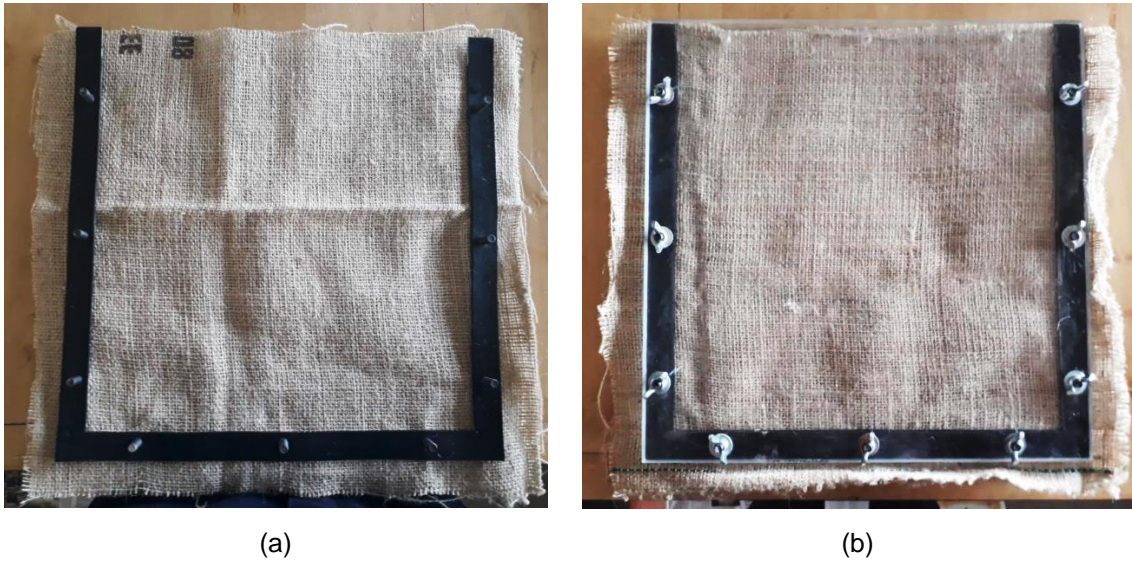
Moldes acrílicos utilizados para a moldagem das placas: a) Sistema de vedação com anéis de borracha; b) Visão do conjunto com anéis de vedação e conjunto de parafusos e arruelas
